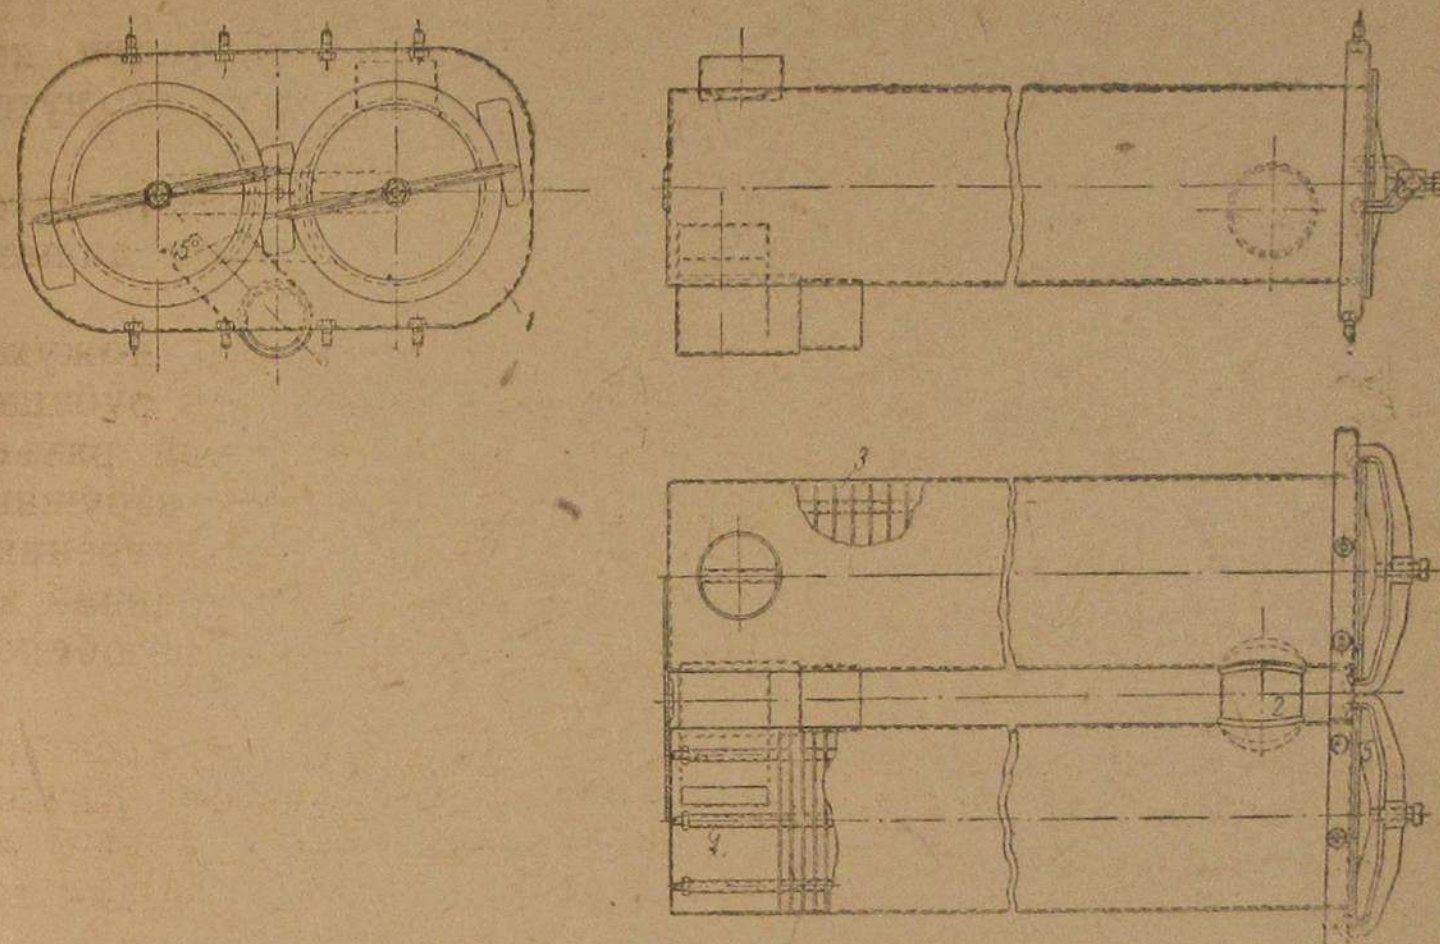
Третий и четвертый цилиндры горизонтального очистителя в сборе.
